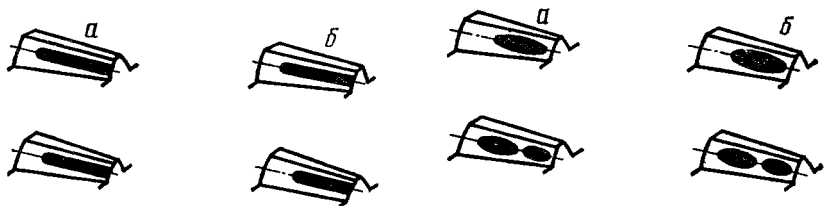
Регулировка зацепления шестерен главной передачи по отпечаткам краски на их зубьях:
